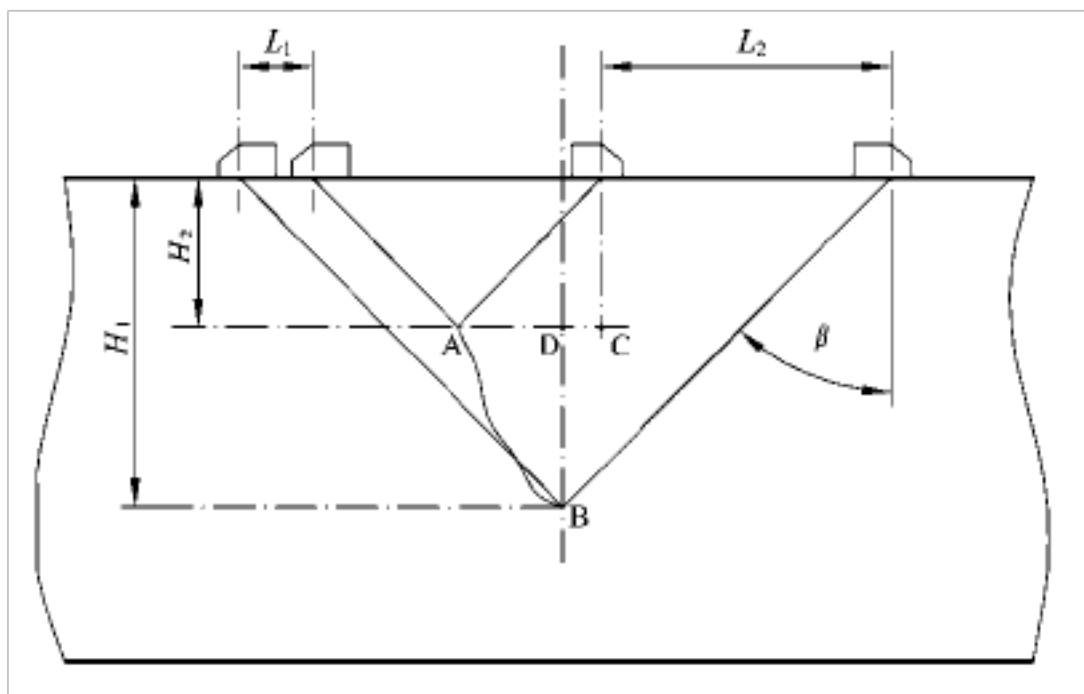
单斜探头对焊接接头内部倾斜缺陷测高方法
